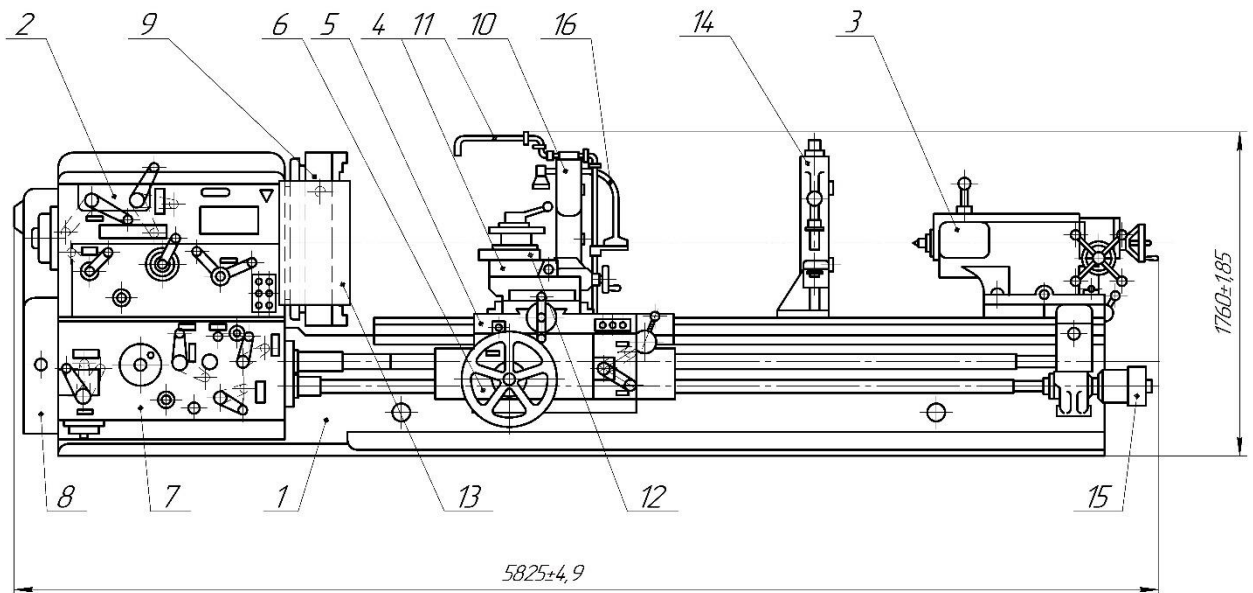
Загальний вид базової моделі верстата 165
